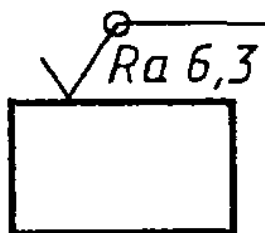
Обозначения шероховатости поверхности, образующей контур
